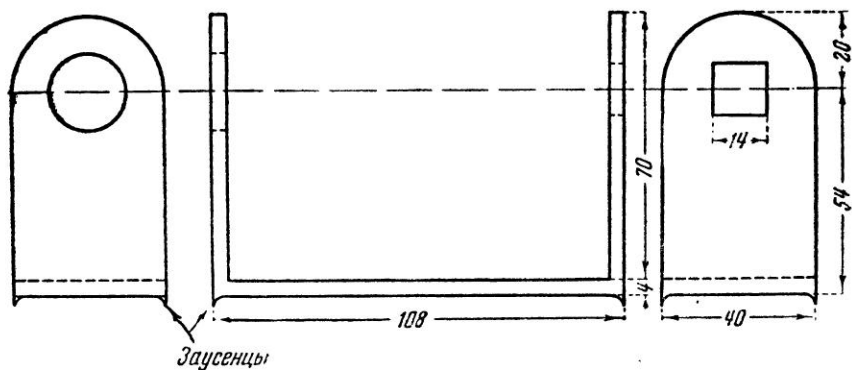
Скоба для крепления неподвижной оси ветроколеса
